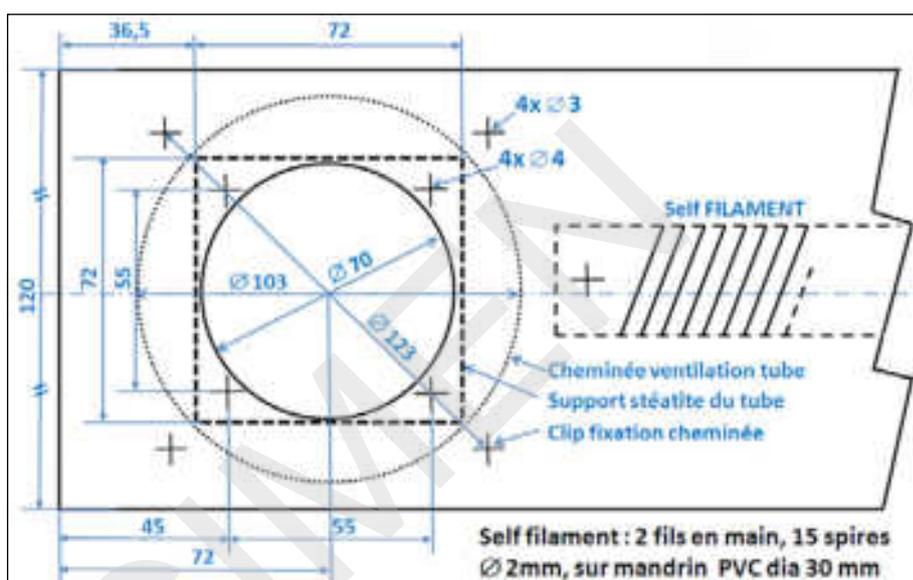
Usinage pour le support tube et la cheminée de refroidissement
